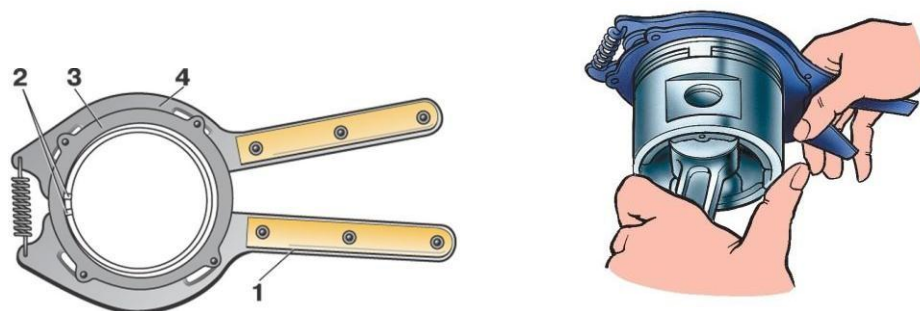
Съемник поршневых колец: 1 – рукоятка; 2 – выступы; 3 – упоры; 4 – захваты
